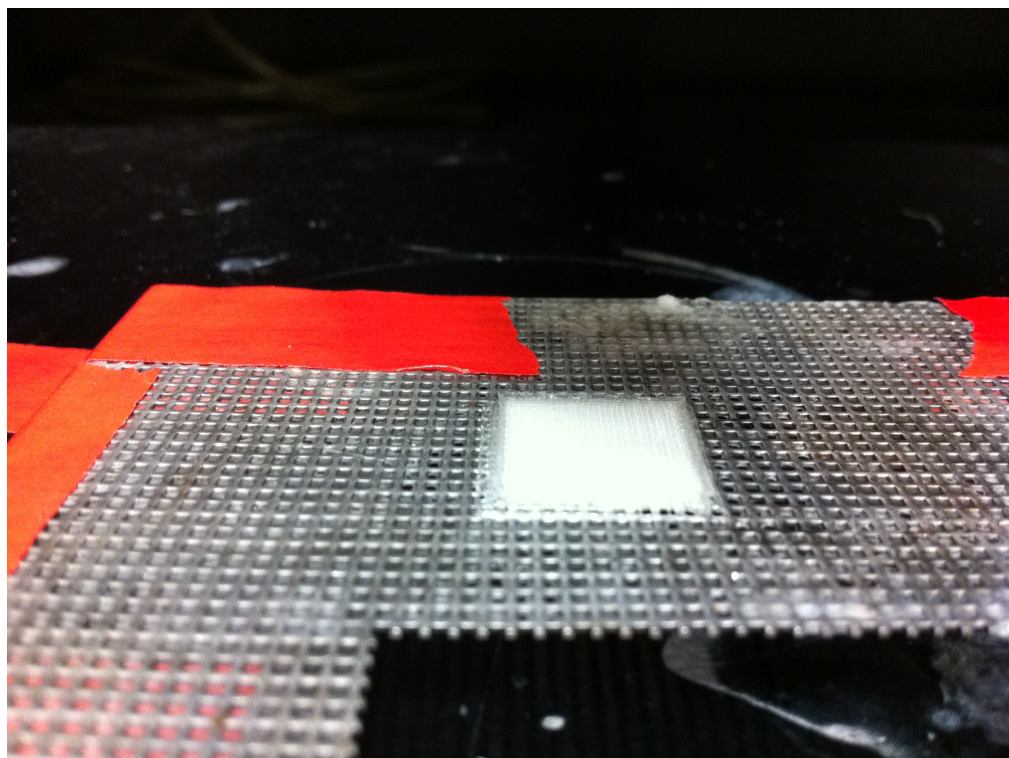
Andamio de PLA fabricado por rapid prototyping.
